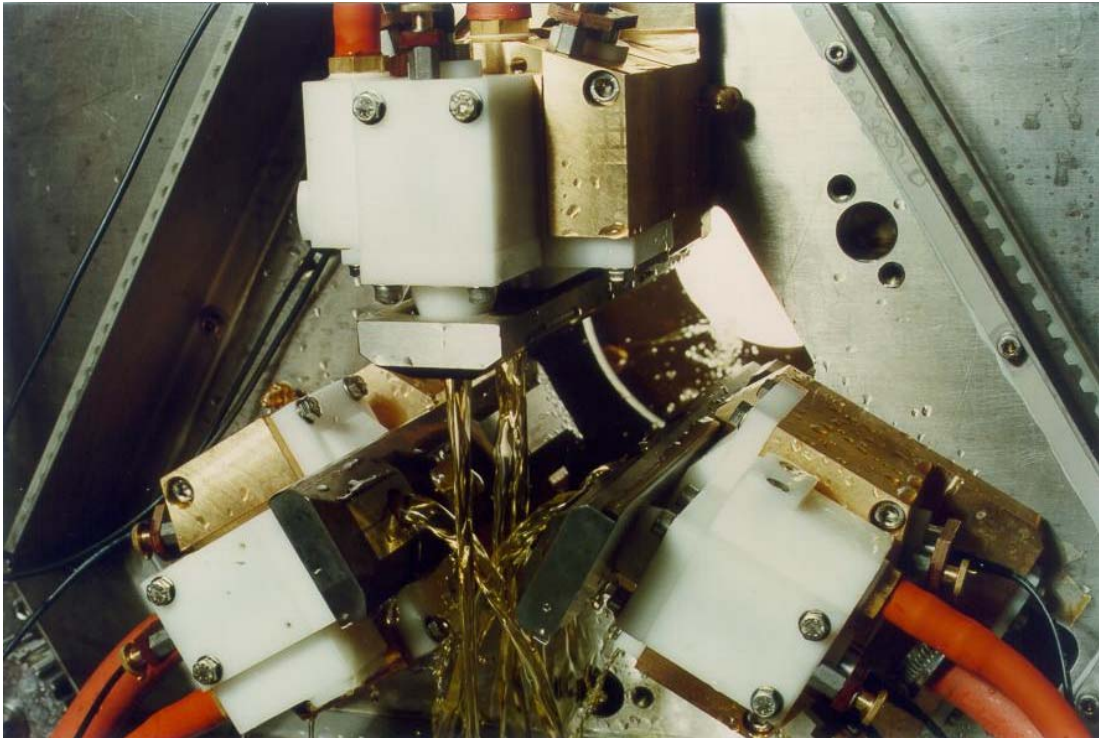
Detailansicht der Prüfkopfträger mit eingeschalteten Wasserstrahlen. Die Führung der Stange erfolgt mit gehärteten Gleitsohlen.
